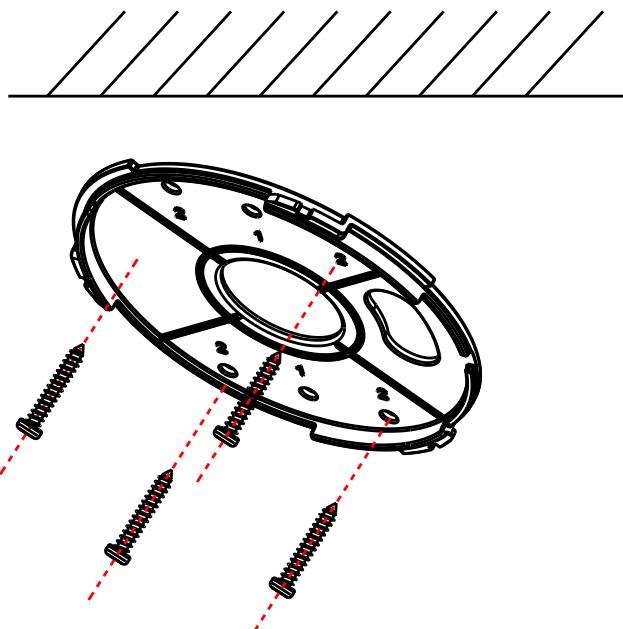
Крепление монтажного основания видеокамеры на потолок / стену
